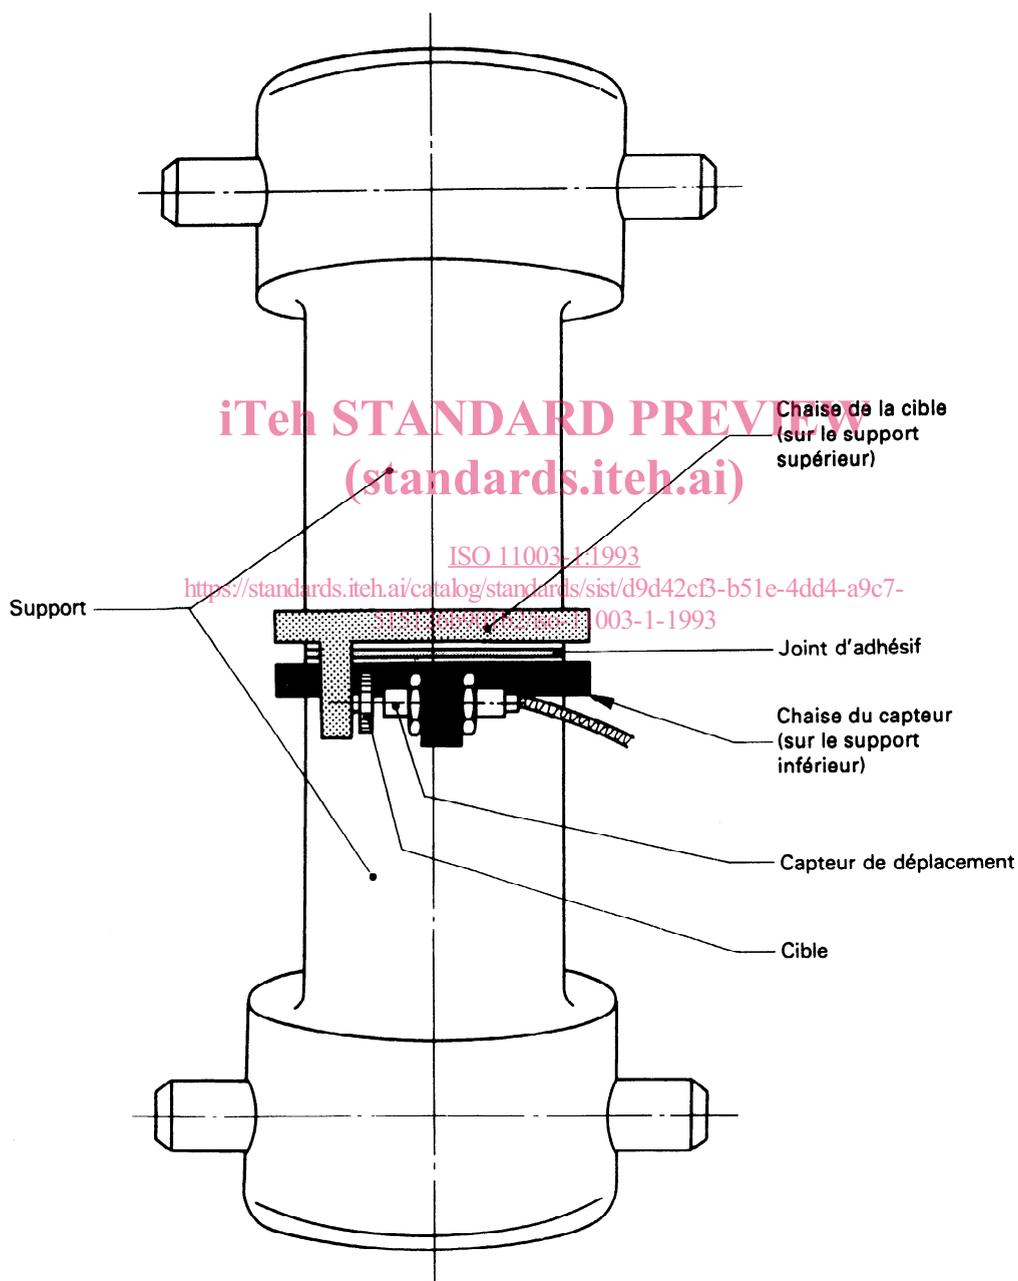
Éprouvette bout à bout, avec le capteur de déplacement, fixée sur la machine d'essai
